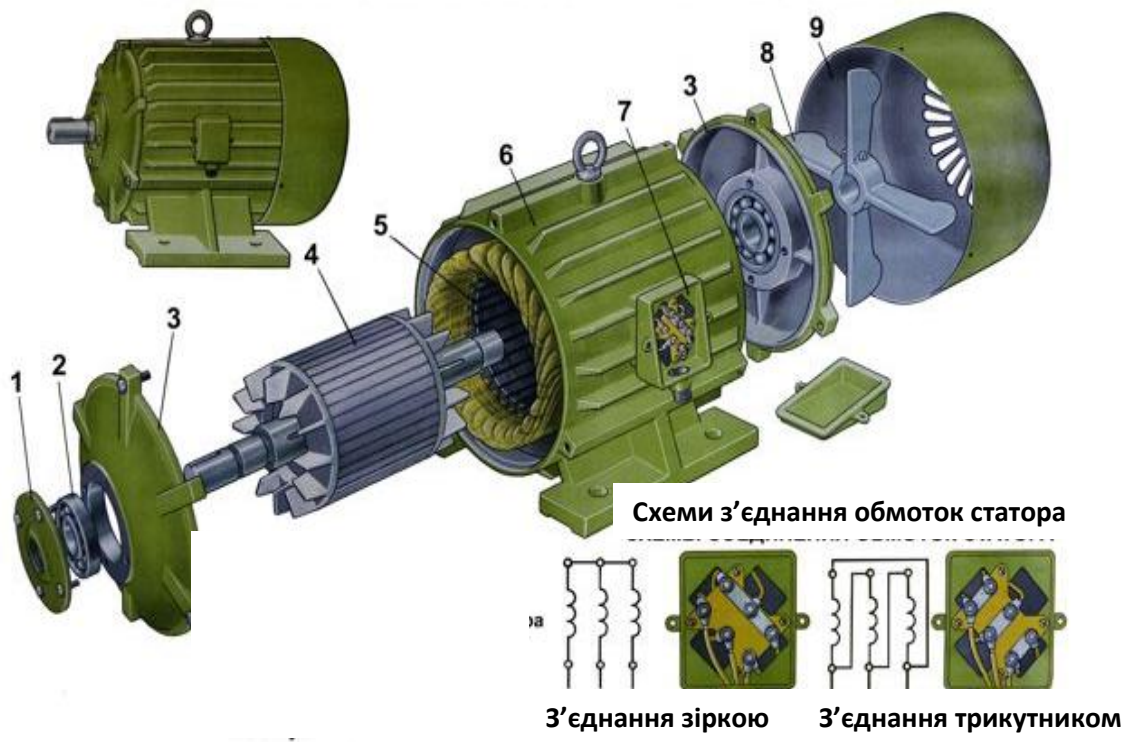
Конструкція асинхронного двигуна: 1 – кришка підшипника; 2 – підшипник; 3 – підшипниковий щит; 4 – ротор з крильцями вентилятора; 5 – статор з обмотками; 6 – станина; 7 – коробка затисків; 8 – вентилятор; 9 – кожух.
